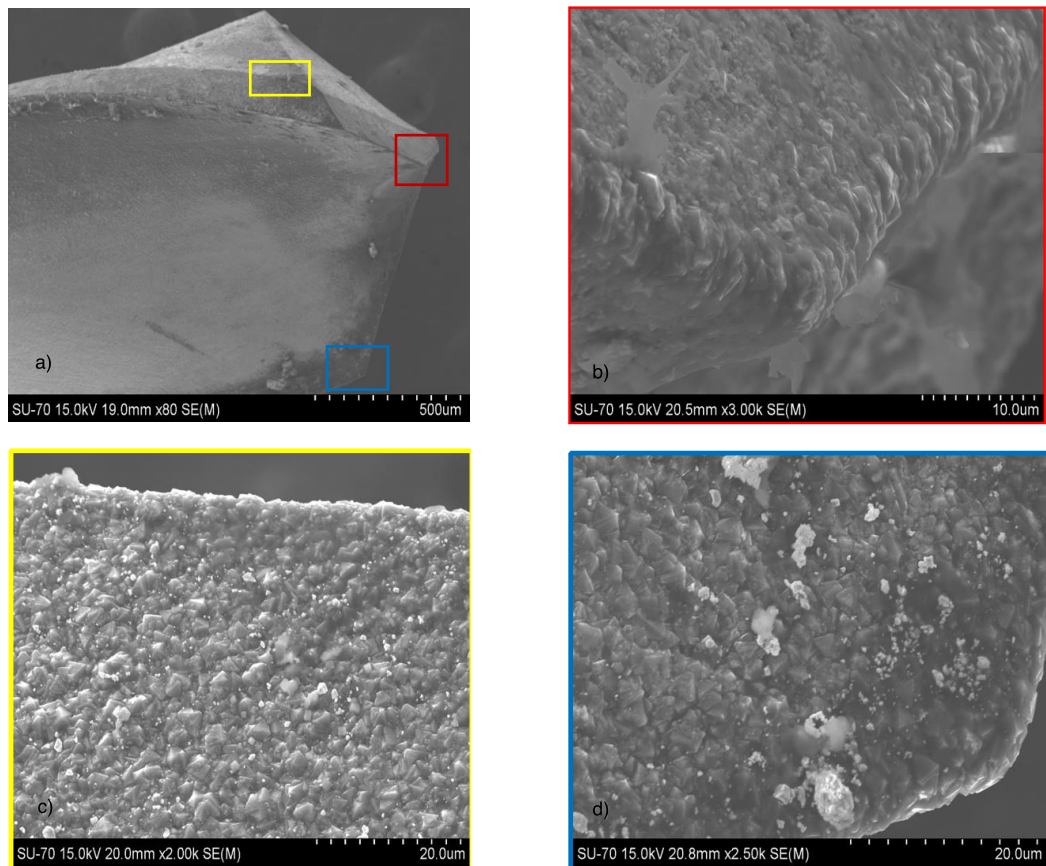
Bloco de metal duro GD16 após testes de furação com uma broca de  $\varnothing$  1.3 mm revestida diamante CVD.
